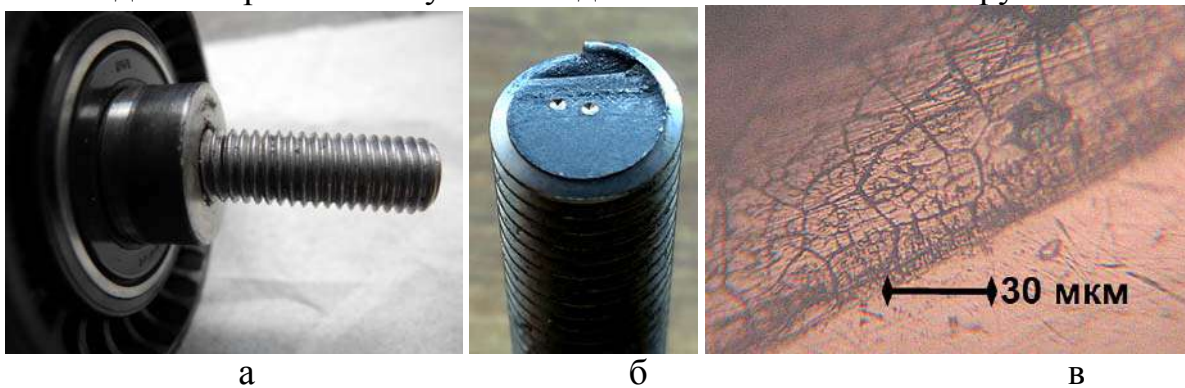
Внешний вид разрушения болта крепления ролика ГРМ (а), излом его стержня (б) и структура металла (в)
